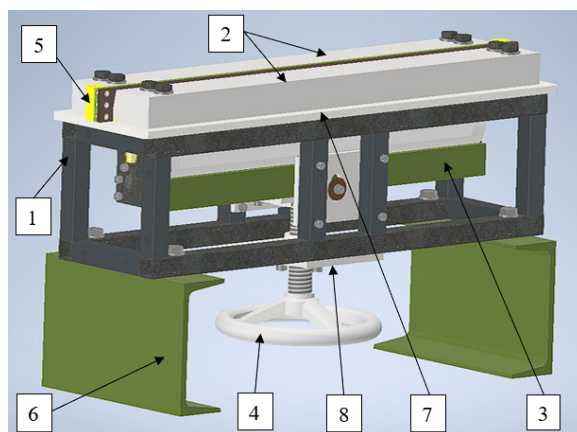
3D-модель струбцини для виготовлення плоских та циліндричних зразків з тонколистового матеріалу: 1 – рама; 2 – притискні планки; 3 – притискач внутрішній (рухомий); 4 – привід рухомого притискача; 5 – пристрій орієнтації зварного стику; 6 – опорні елементи; 7 – пластина основи; 8 – пластина кріплення гвинта
